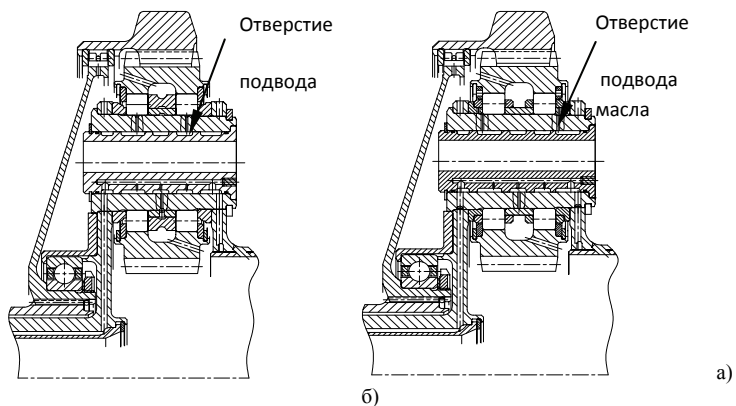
Схема подвода смазки в подшипники главного редуктора двигателя ТВЗ-117ВМА-СБМ1: а – исходная конструкция; б - доработанная конструкция подшипника сателлита
